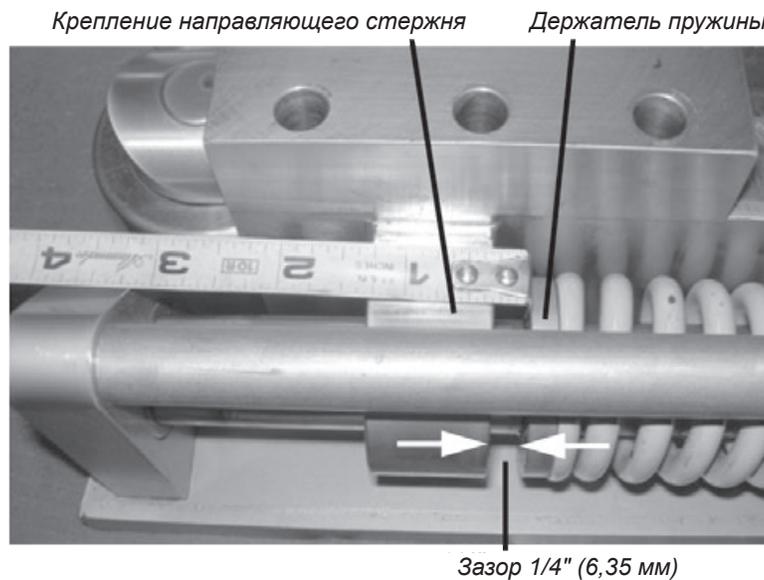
Выставьте суппорт для получения зазора 1/4" (6,35 мм) между креплениями направляющего стержня и держателями пружины.
